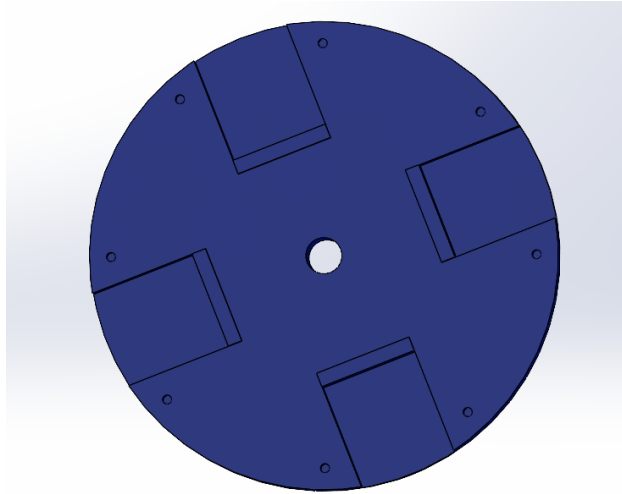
Vista superior del chasis diseñado en SolidWorks.
